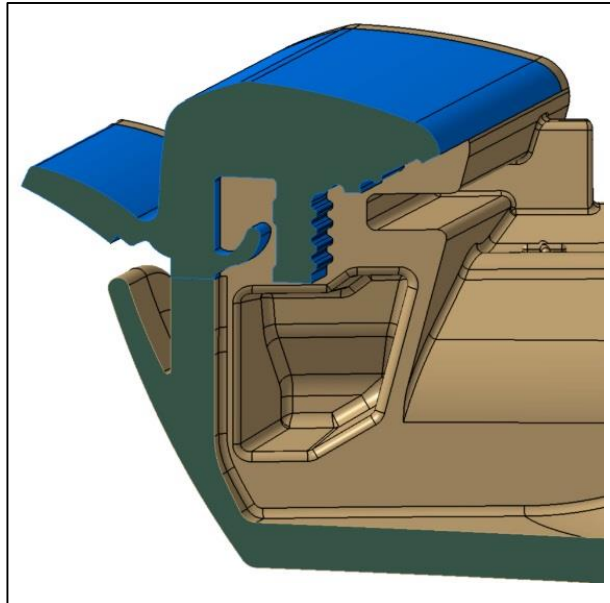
Upevňovací výstupek pro vrut na integrovaném dělicím sloupku
